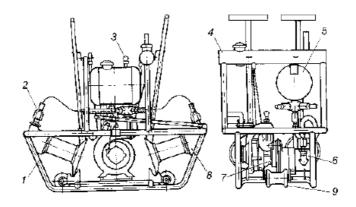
Схема моторного гидравлического рихтовщика [8]: 1 — рама; 2 — изоляция рамы от цилиндров; 3 — регулятор давления; 4 — топливный бак; 5 — масляный бак; 6 — насос; 7 — двигатель; 8 — гидравлический цилиндр; 9 — ролик для перемещения по рельсу
